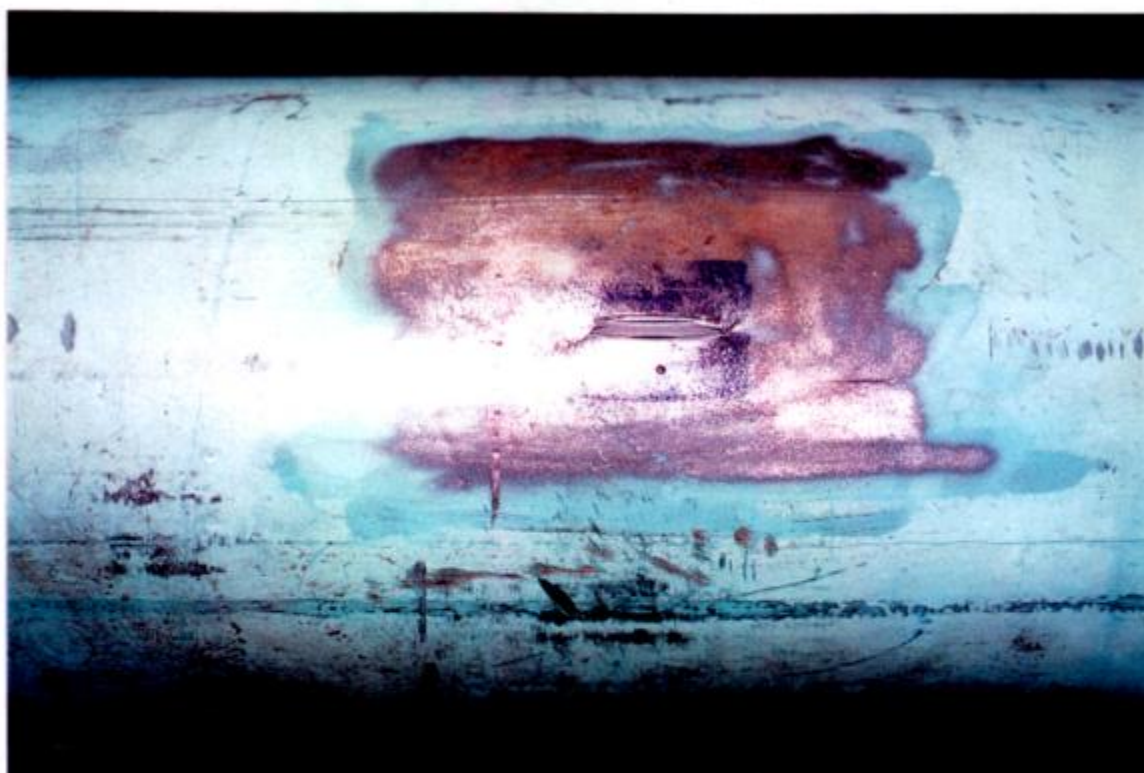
Aspecto de la fractura en la probeta 3 (tubo grado X65)
